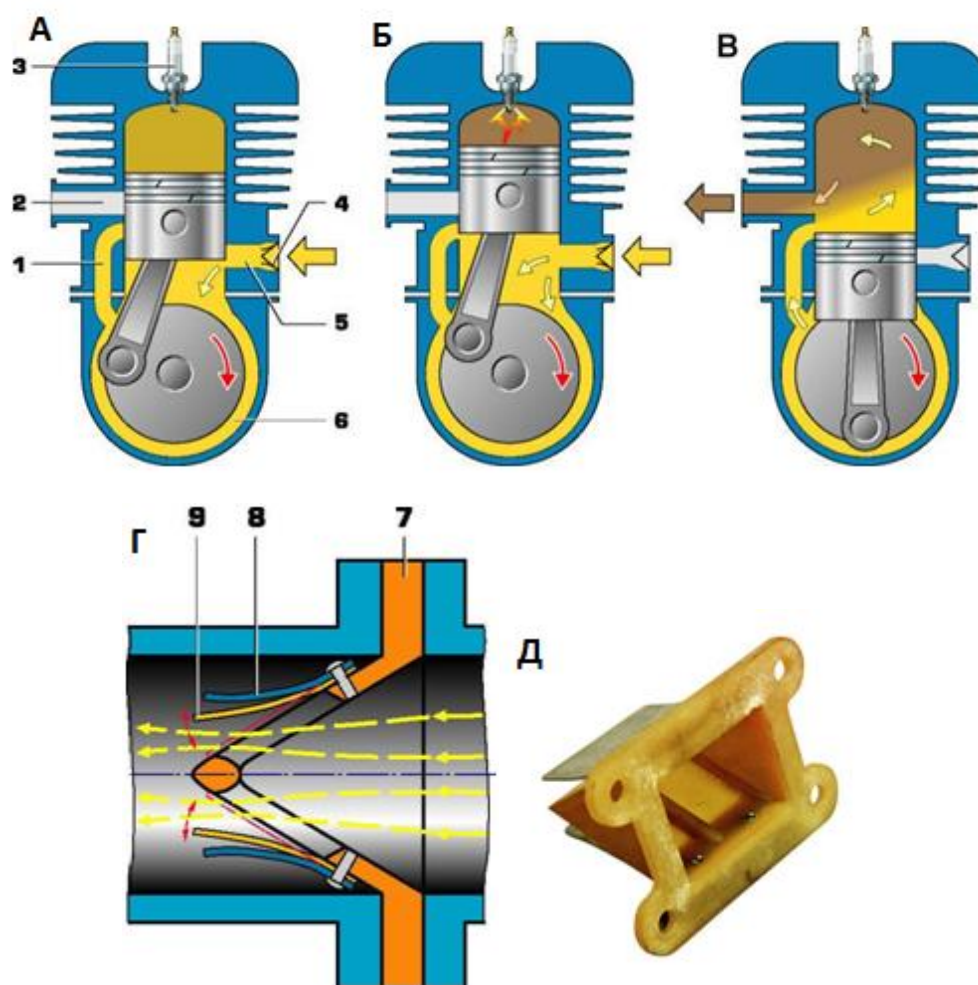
Рабочий процесс двухтактного двигателя:
